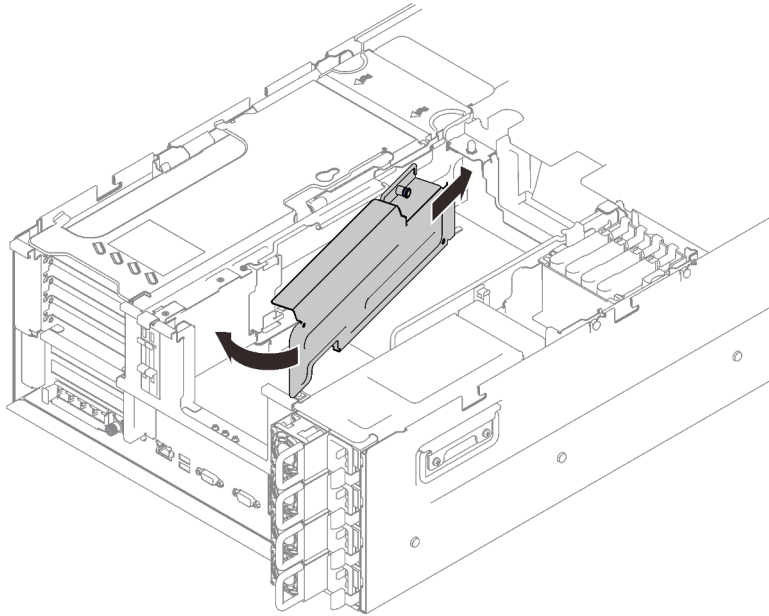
Instalando o backplane M.2 no conjunto de suporte
